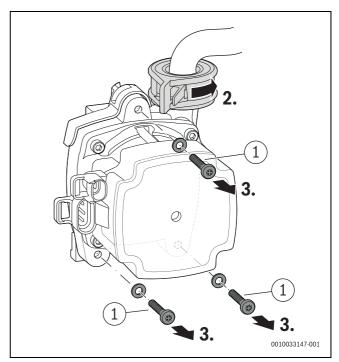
Déverrouiller la pompe de chaudière et retirer les vis
